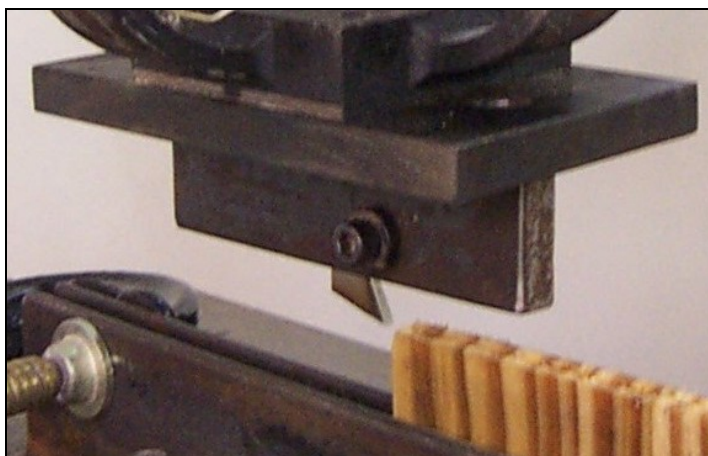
Suporte da ferramenta de corte do tipo dente (bedame)
